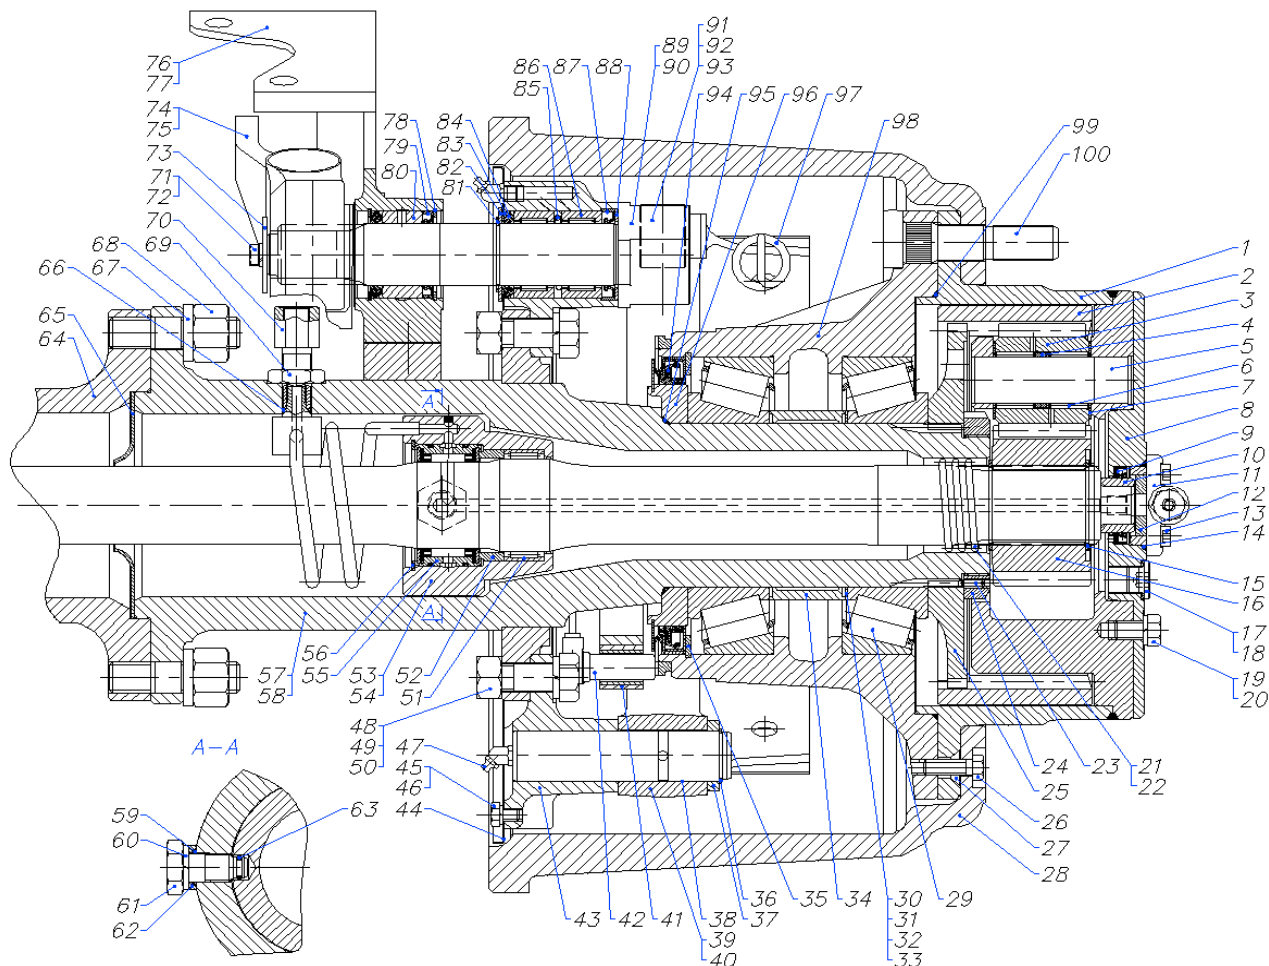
Тормозной механизм и колесный редуктор – вариант со сваренным корпусом колесного редуктора
